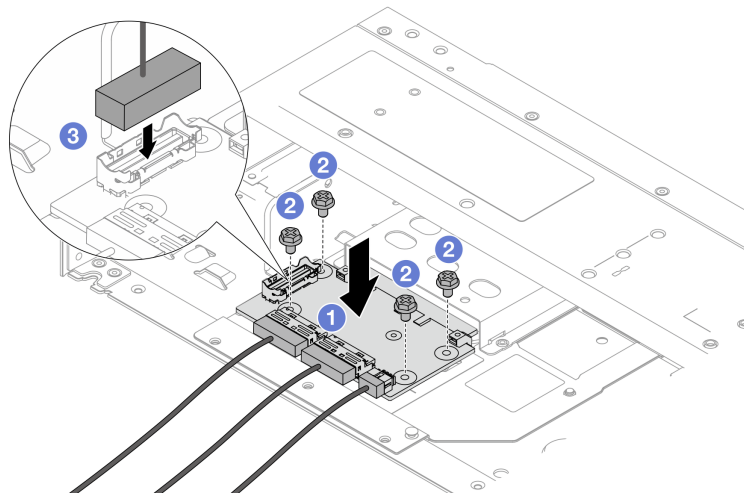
Instalación de la tarjeta de interposición de OCP frontal
